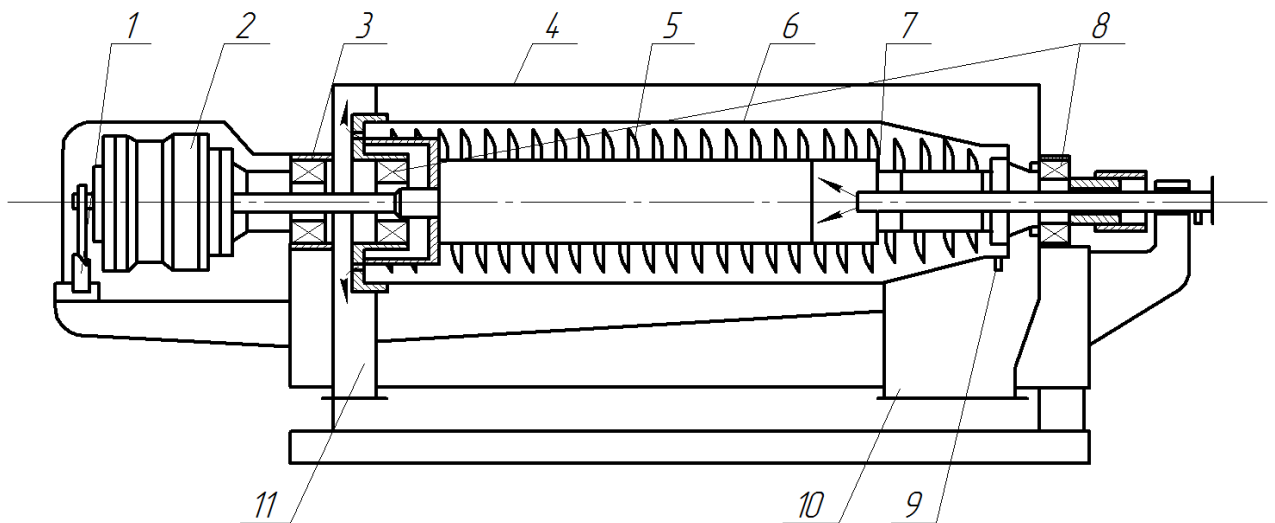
Схема осаджувальної центрифуги типу ОГШ: 1 – захисний пристрій; 2 – редуктор; 3 – опорний підшипник шнека; 4 – кожух; 5 – шнек; 6 – ротор; 7 – живить трубопровід; 8 – опорний підшипник ротора; 9 – розвантажувальне вікно; 10 – камера вивантаження осаду; 11 – камера відводу фільтрату
